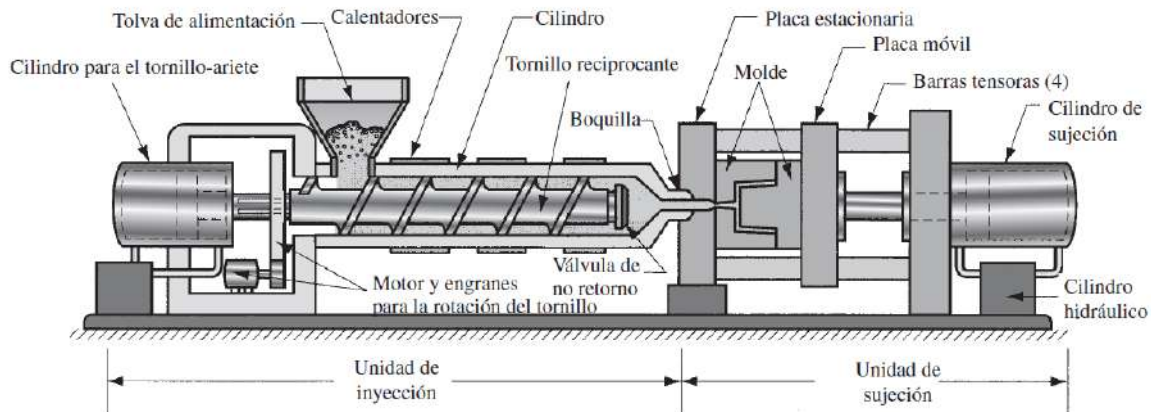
máquina de moldeo por inyección, del tipo de tornillo recíprocante [1]
